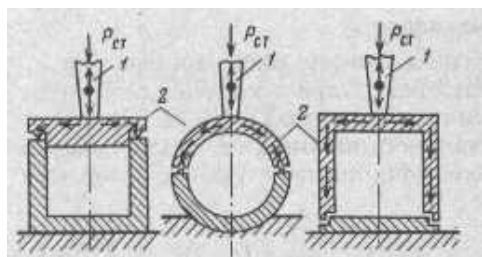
Схема передачной ультразвуковой сварки: 1 – волновод-инструмент; 2 – свариваемое изделие
